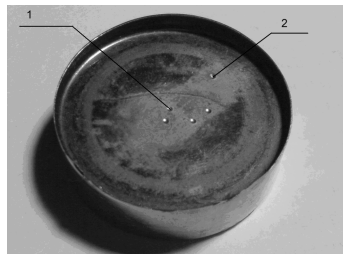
Испытание на прочность по Бринеллю каленым шариком с обратной стороны точной заготовки детали «Дно». 1 – в центре; 2 – на периферии.
